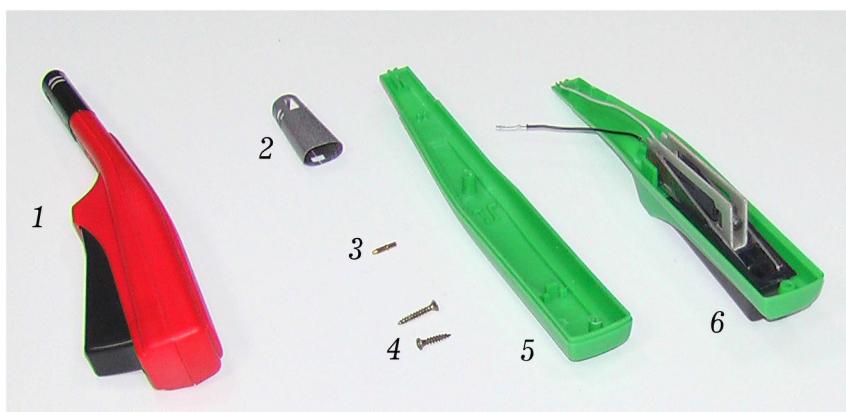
Пьезозажигалка в сборе и со снятой крышкой корпуса
